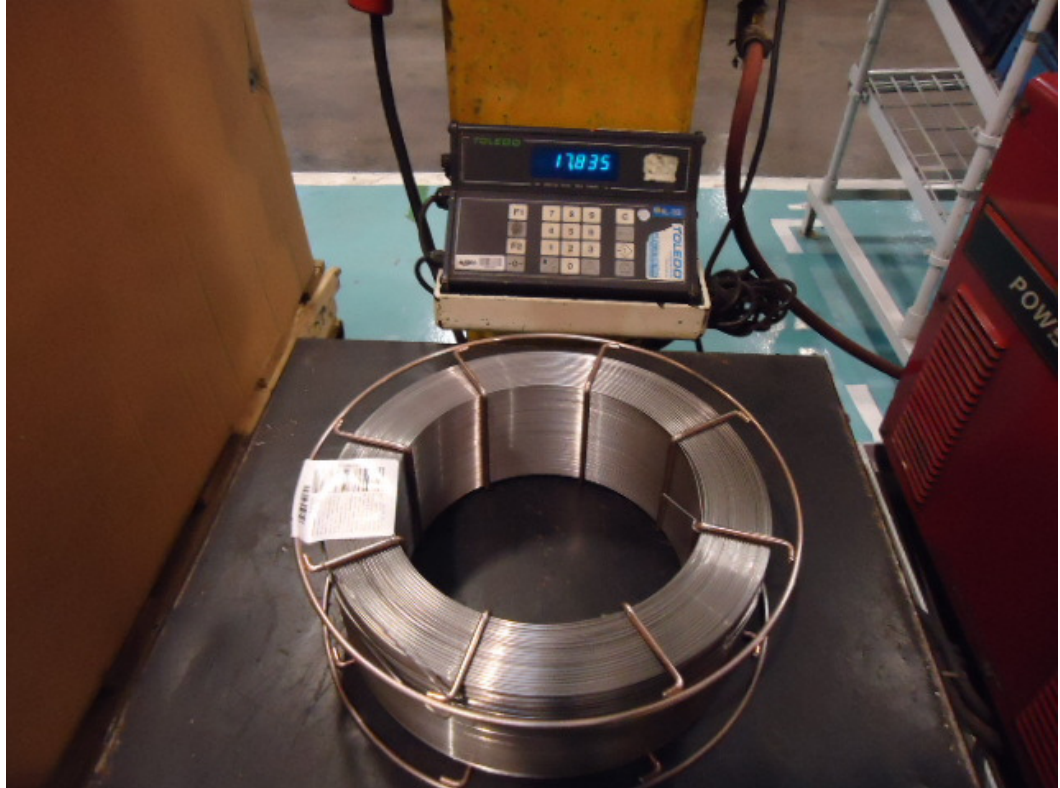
Arame após a soldagem com mistura 10% CO₂
